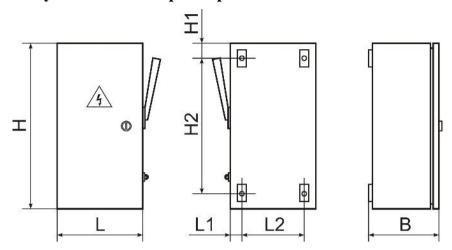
Общий вид и габаритные размеры ящиков силовых
